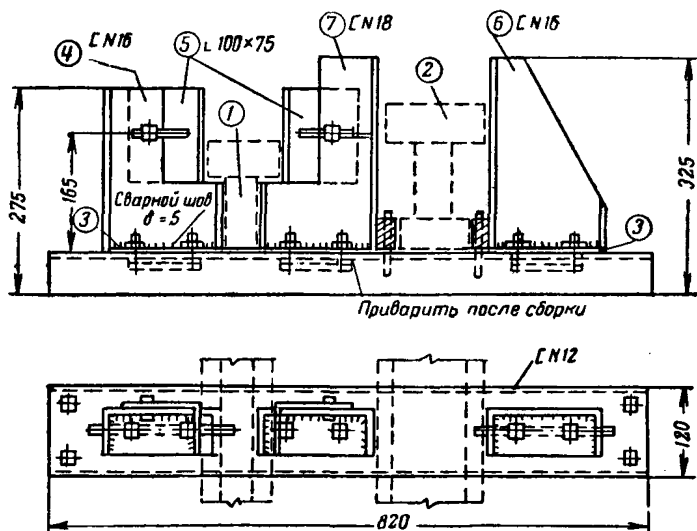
Универсальная обойма для сборки двутавровых балок при гвоздевой запрессовке
